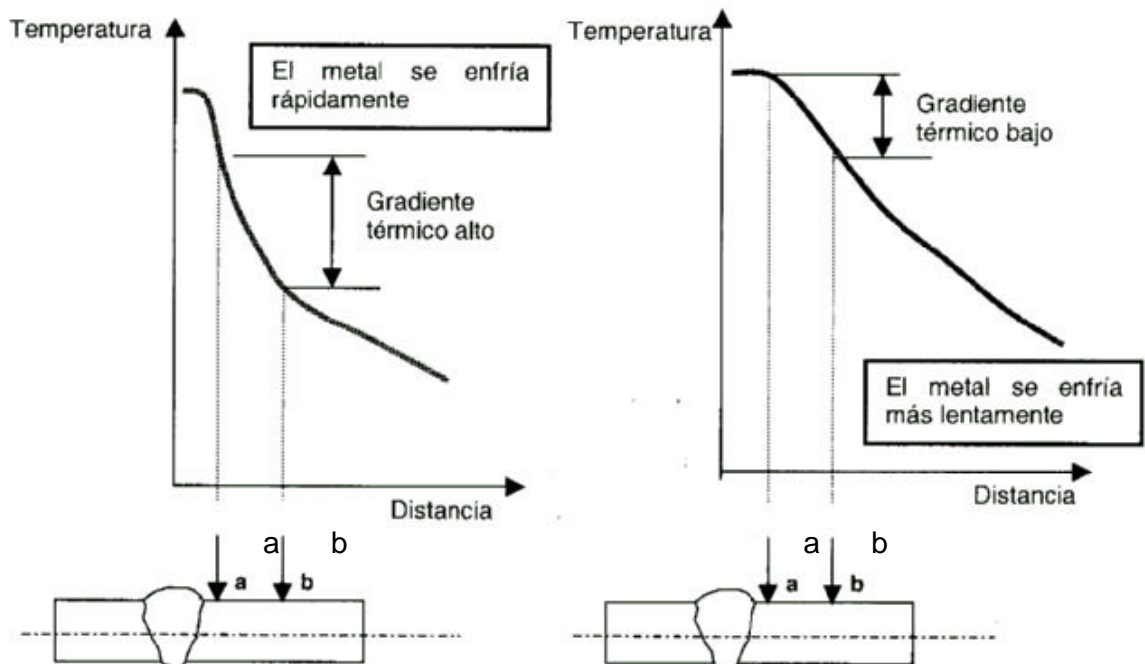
GRADIENTES DE TEMPERATURAS EN UNA UNIÓN SOLDADA QUE SE PRESENTA ENTRE DOS PUNTOS CUALESQUIERA DE LA PIEZA A SOLDAR
